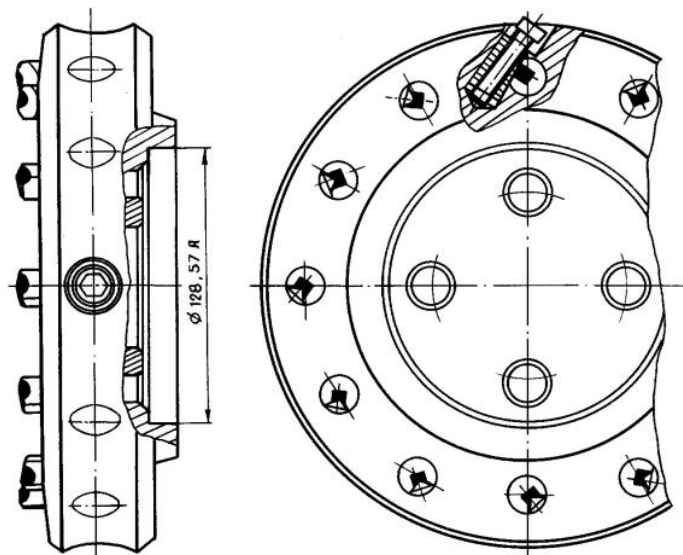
Торцева ступінчаста фреза косокутного різання для обробки відкритих поверхонь
